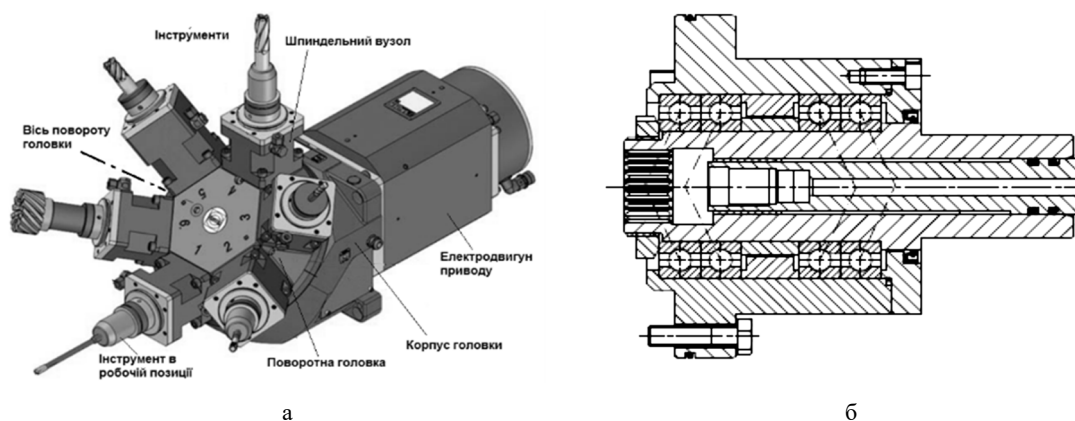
Револьверна головка типу корони “Sauter”: а – загальний вигляд; б – шпиндельний вузол
